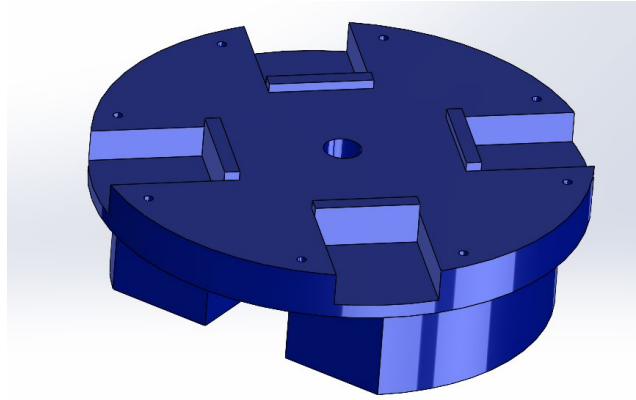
Vista isométrica del chasis del vehículo diseñado en SolidWorks.
